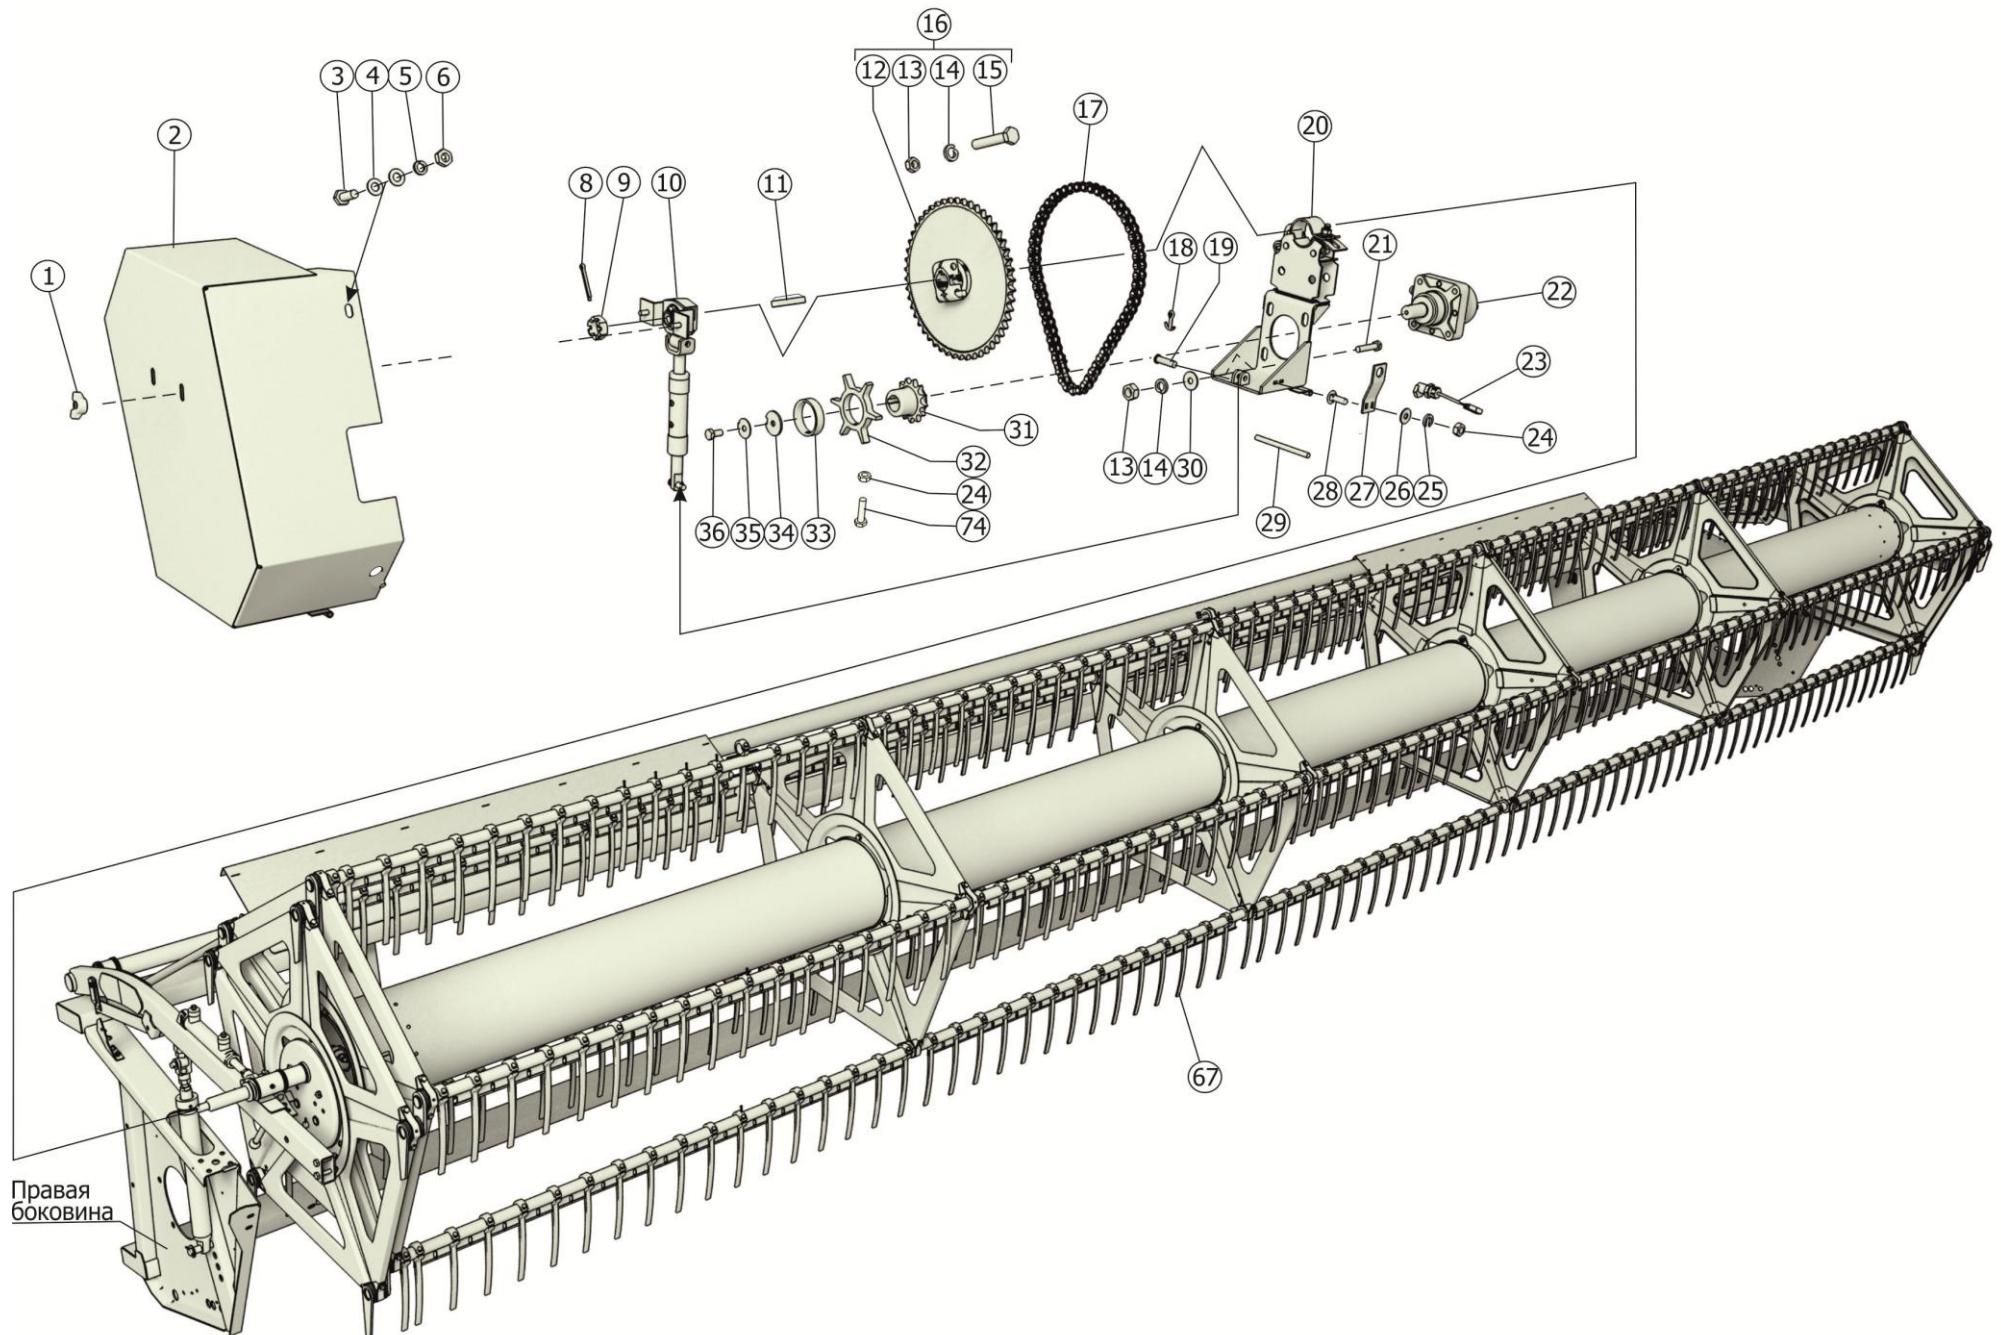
Установка мотовила ЖСУ-900.03.00.000. Вид справа
